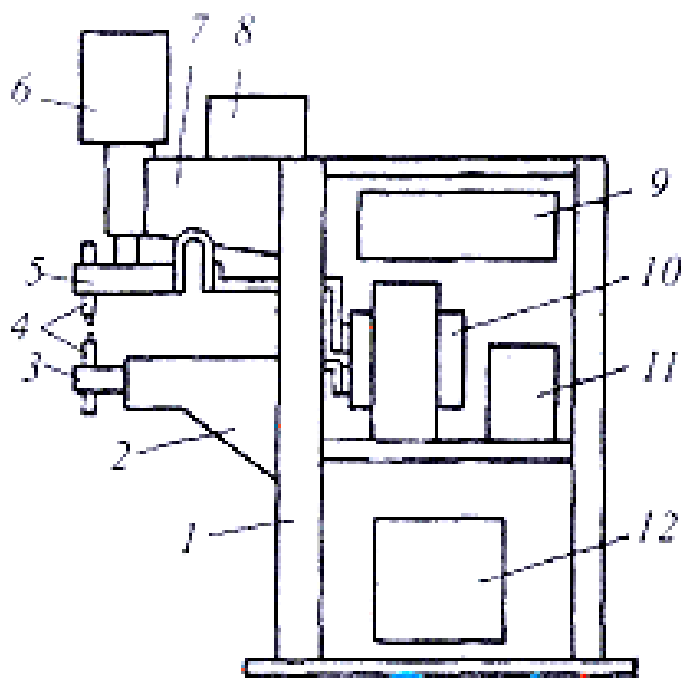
Основные узлы машины для точечной сварки
